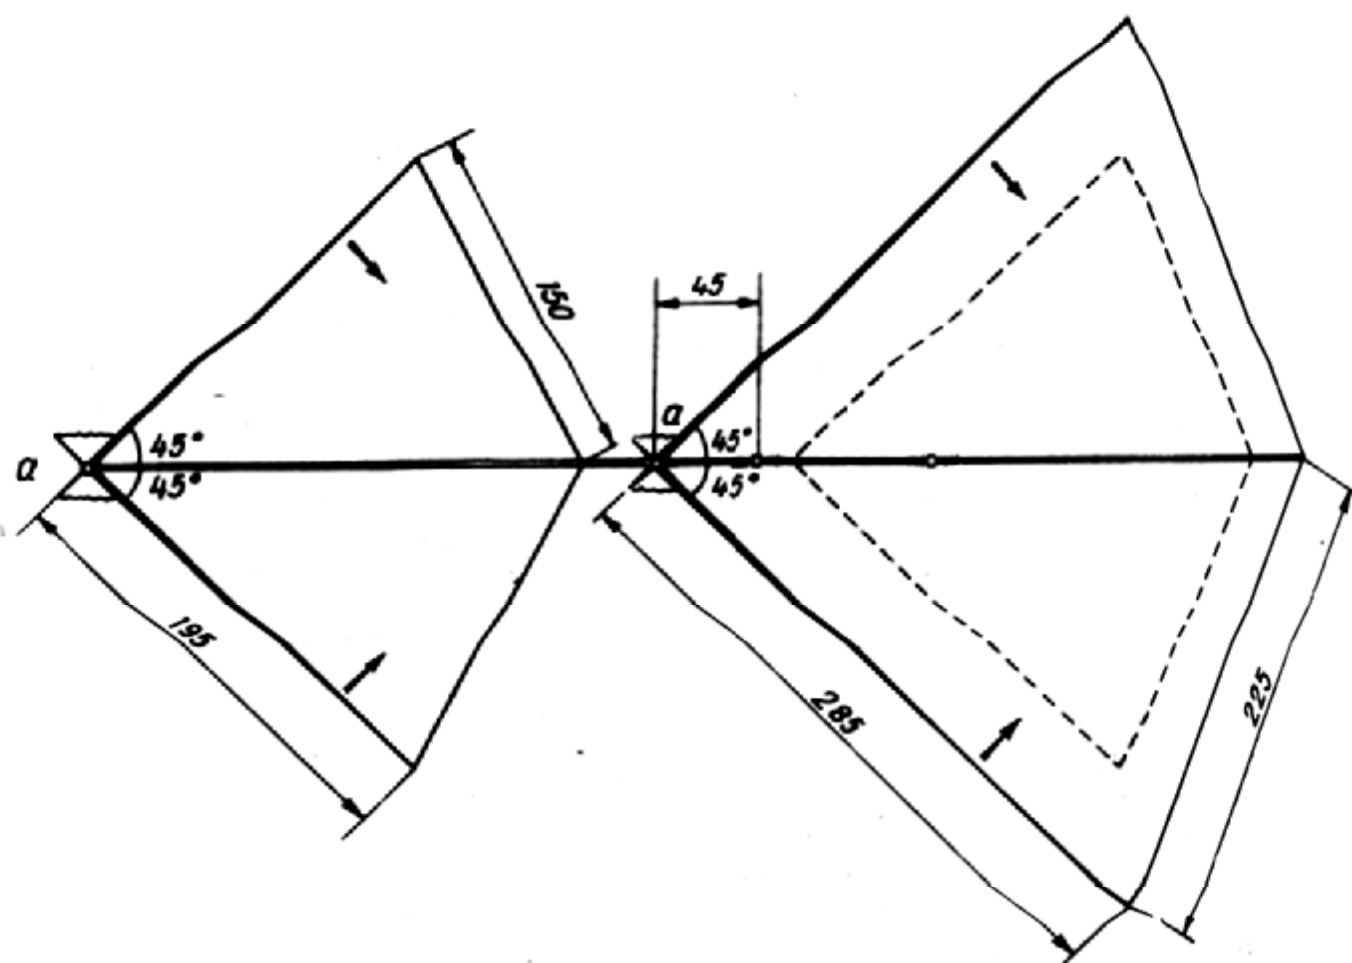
Модель ракетоплана типу «Качка» (креслення в плані); а) механізм розкриття крила й стабілізатора.
